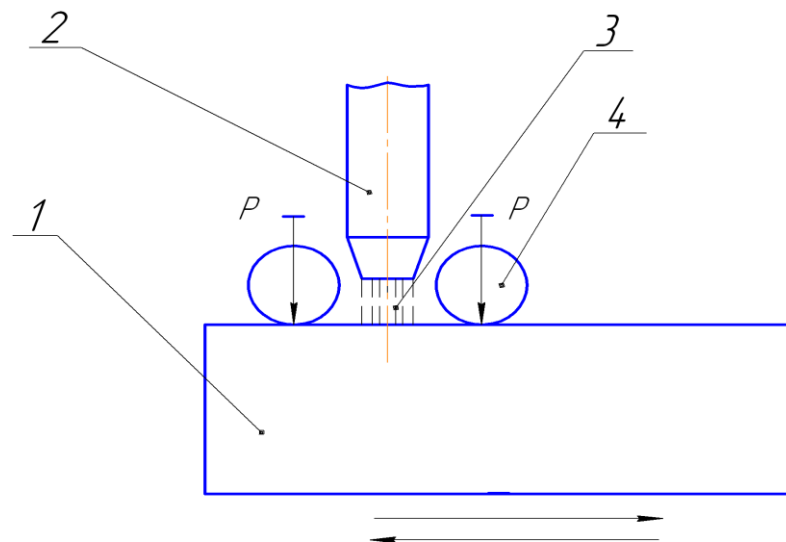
Струминна обробка попередньо напружених поверхонь.
